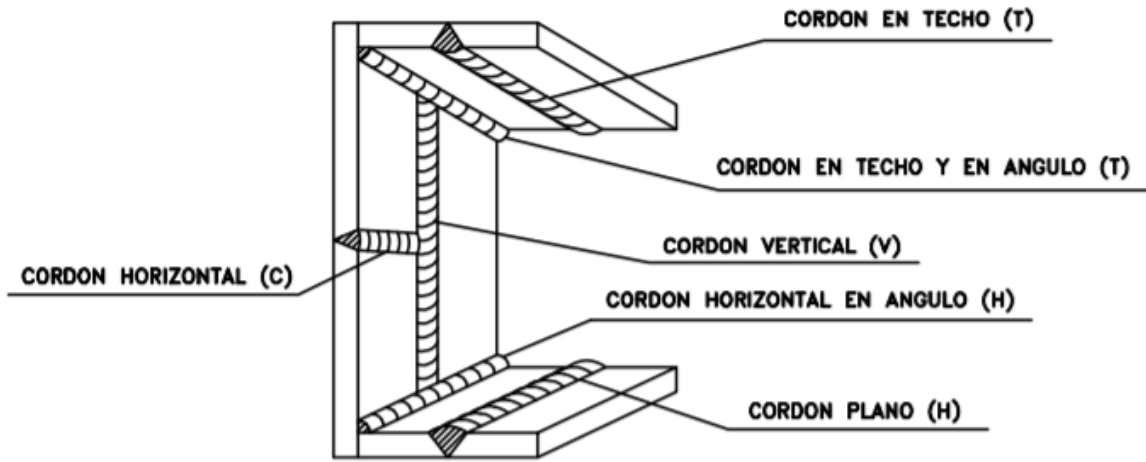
Clasificación de los cordones de soldadura según su posición durante el proceso de soldadura
